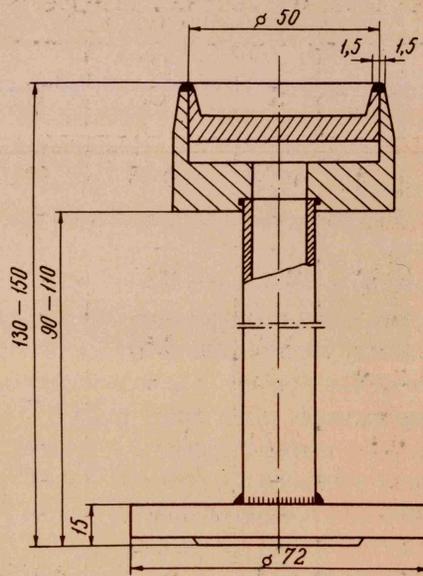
Общий вид образца для испытаний металла шва на вакуумную прочность
